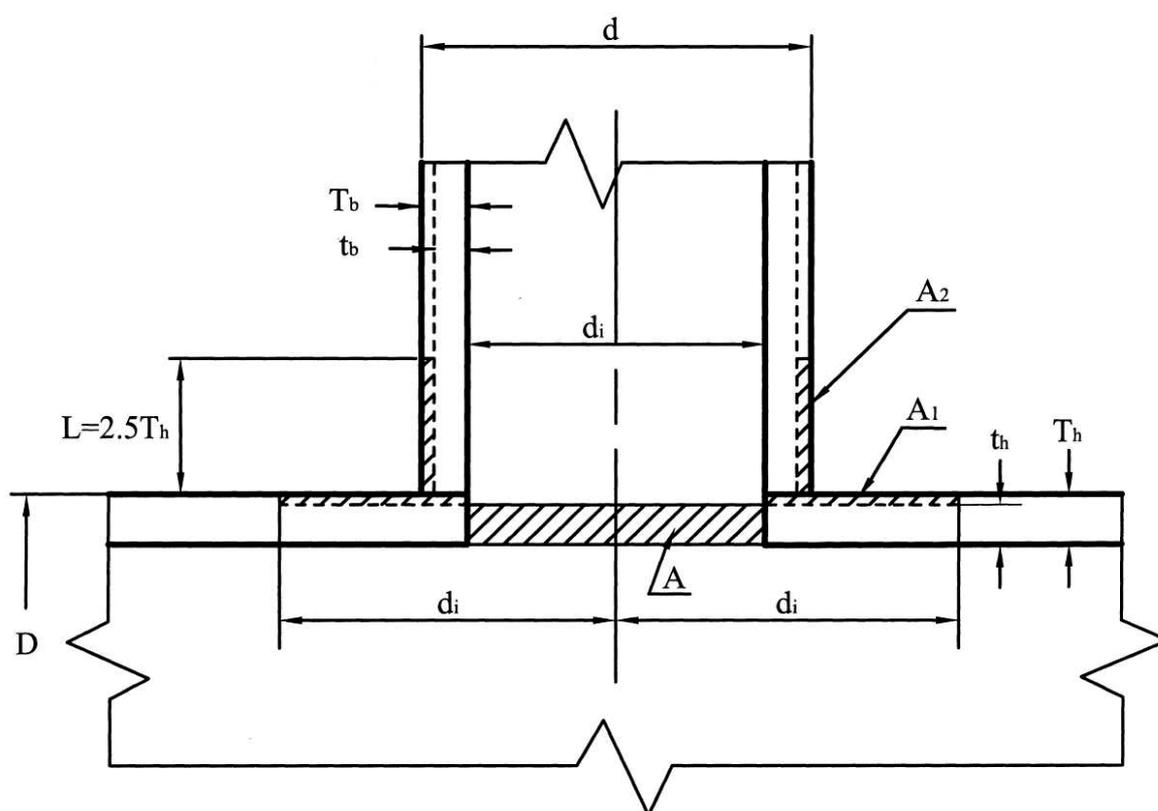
Схема для расчета сварного тройника
